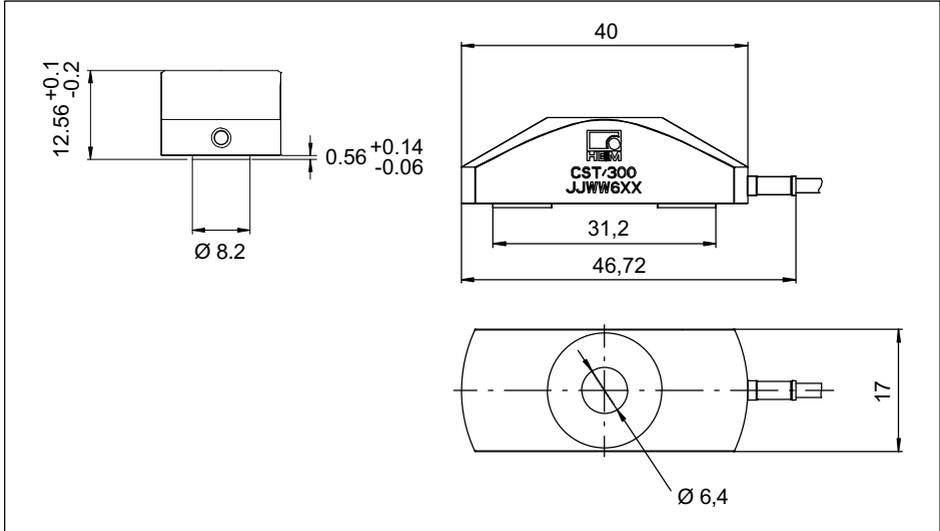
Dimensioni del sensore di deformazione CST/300
